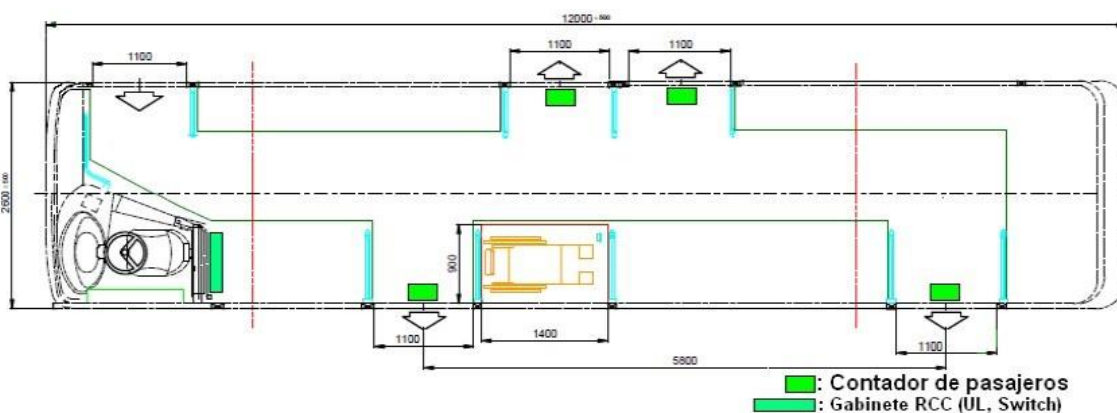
Ubicación de las platinas para los contadores de pasajeros
